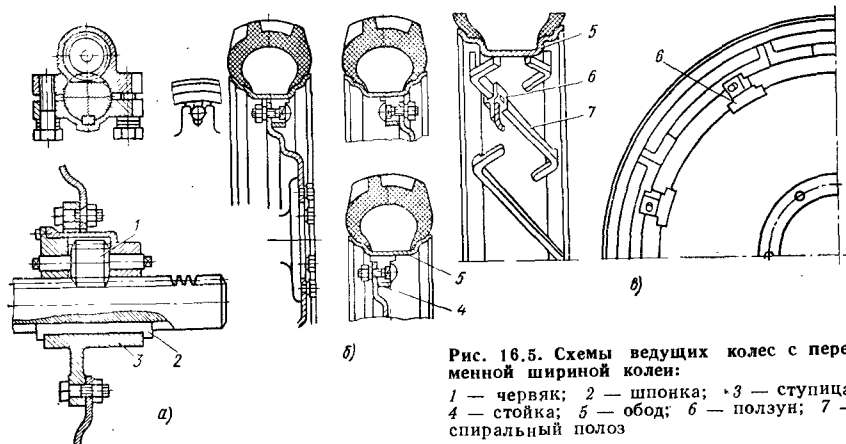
Схемы ведущих колес с переменной шириной колеи:
